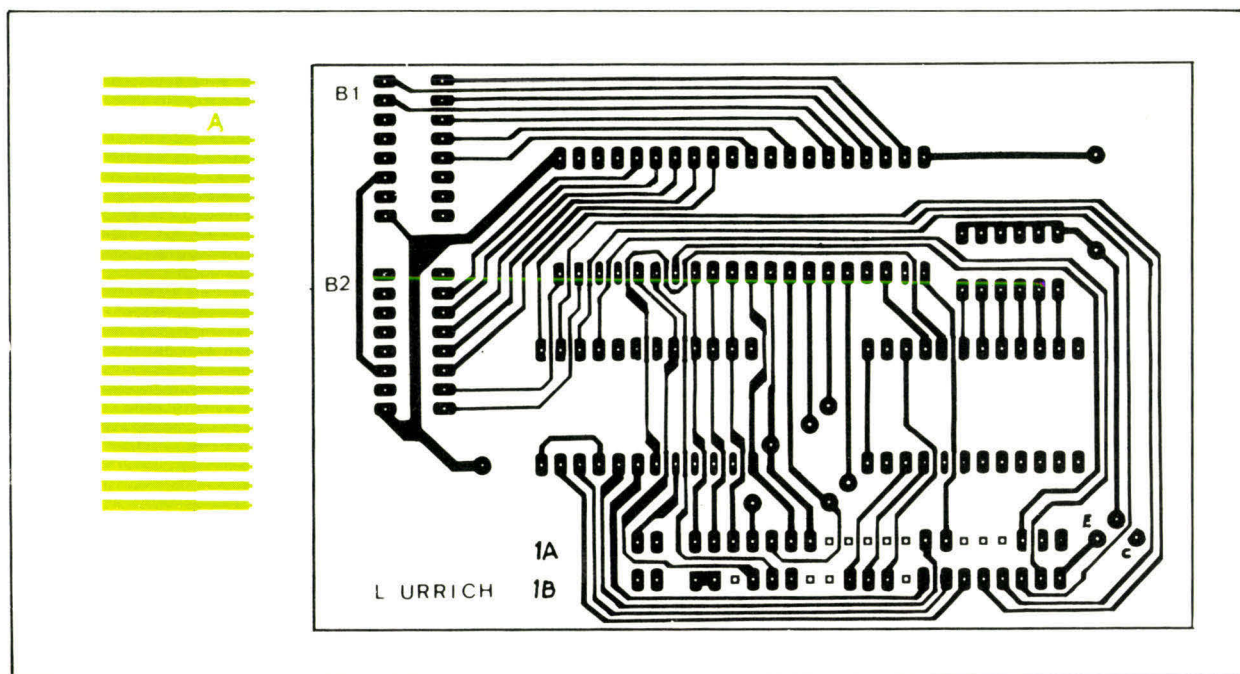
Circuit imprimé vu côté « SOUDURES ». (Ech. 1)
